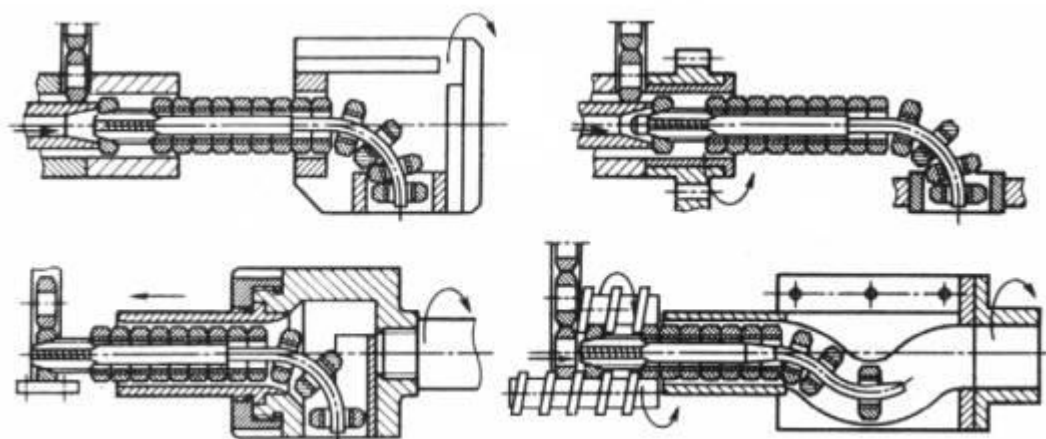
Принципова схема вузла формоутворення внутрішнього різьблення популярних гайконарізних автоматів
